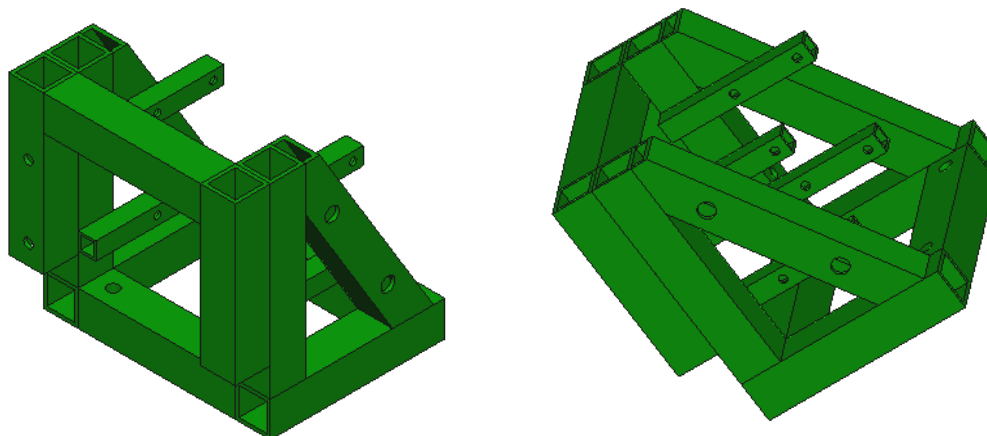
Estrutura final para o suporte do motor com a caixa redutora desenhada no SolidWorks.
